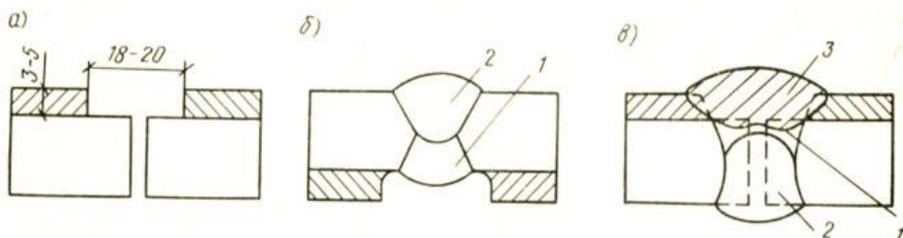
Сварка двухслойной стали без разделительного слоя а - подготовка кромок под сварку; б - сварка основного металла; в - сварка облицовочного металла; 1, 2 - слои основного металла; 3 - облицовочный слой
